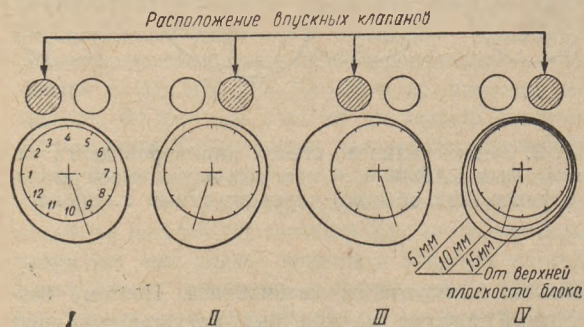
Эпюры износа стенок цилиндров двигателя автомобиля ГАЗ-ММ при впуске смеси через впускные клапаны (опытный двигатель).
